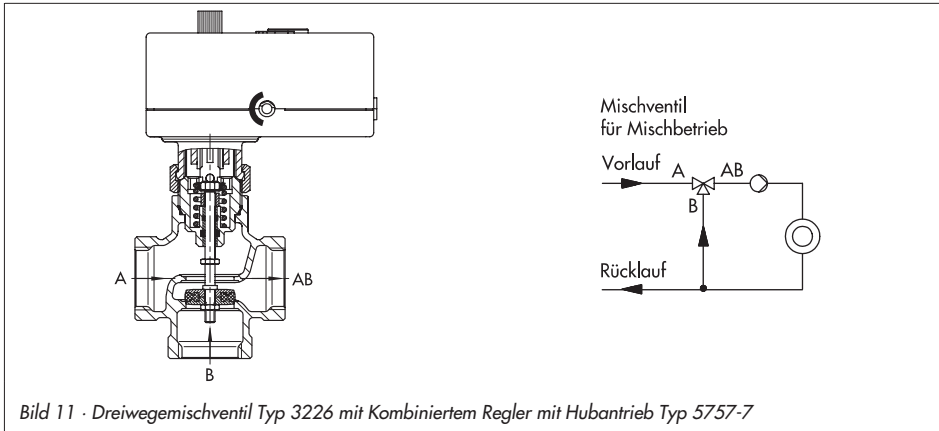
· Dreiwegemischventil Typ 3226 mit Kombiniertem Regler mit Hubantrieb Typ 5757-7
